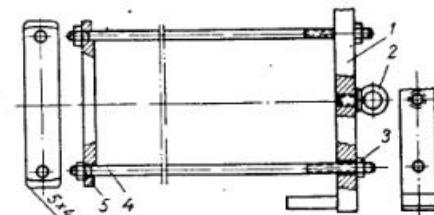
Приспособление для выпрессовки цилиндровых втулок двигателей типа NVD-48 и NVD-36:
